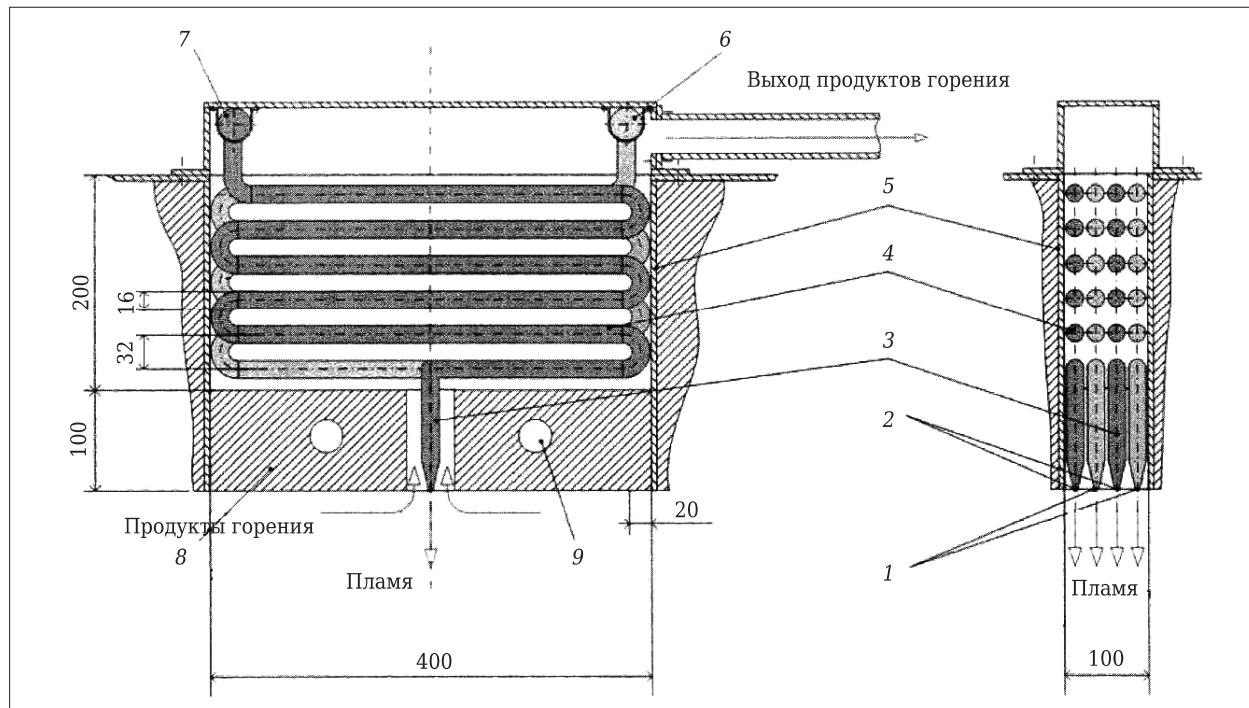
Горелочно-рекуперативный блок: 1 — сопла для богатой газовоздушной смеси; 2 — сопла для бедной газовоздушной смеси; 3 — сопловая труба; 4 — петли рекуператора; 5 — камера рекуператоров; 6 — коллектор богатой газовоздушной смеси; 8 — горелочный камень; 9 — стальные поддерживающие стержни
